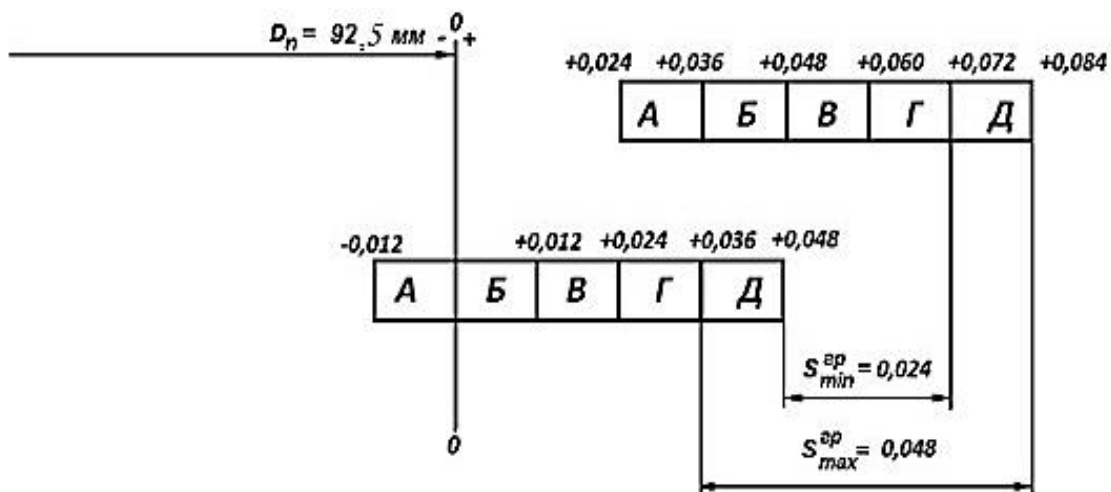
Схема розташування полів допусків з'єднання «Поршень - гільза» двигунів ЗМЗ-402 за п'ятьма групами
